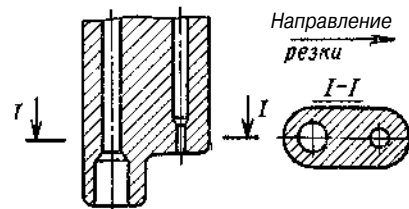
Последовательное расположение подогревающего и режущего сопла
